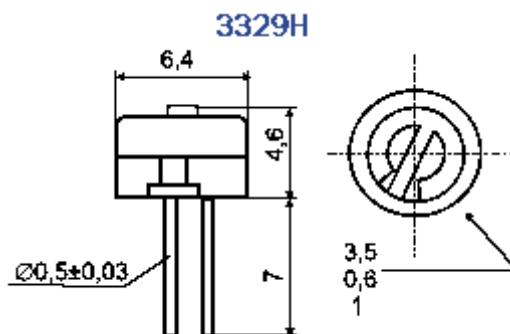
Підлаштувального резистора розміри габаритні
